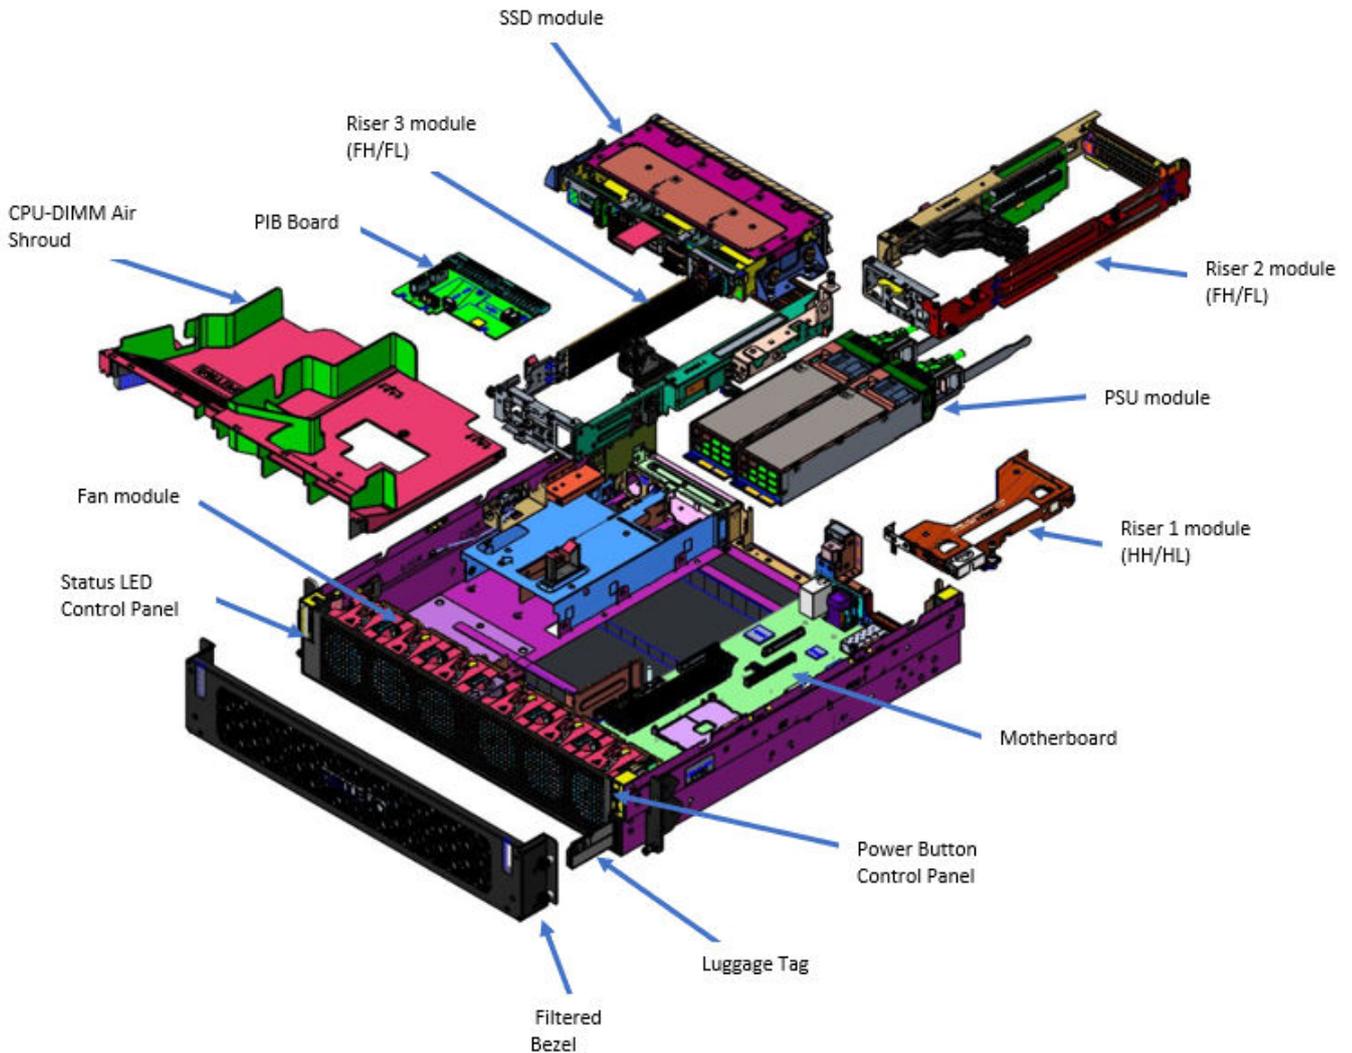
Vue éclatée interne du boîtier XR12 avec accès par l'arrière
